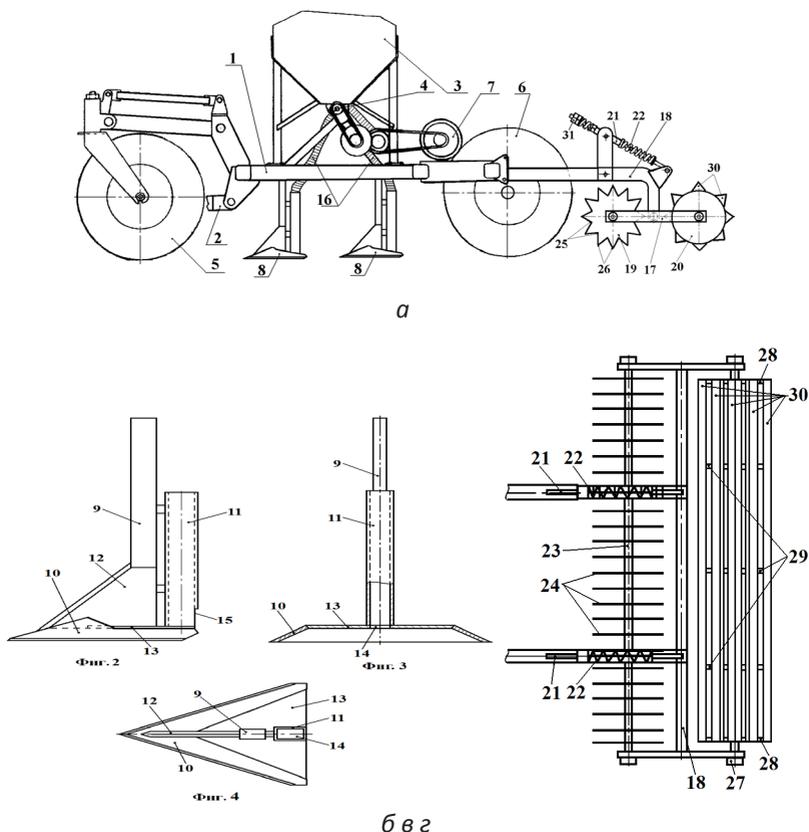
Зерновая сеялка: а - вид сбоку; б – сошник, вид сбоку; в – сошник, вид сзади; г – катковая приставка, вид сверху
